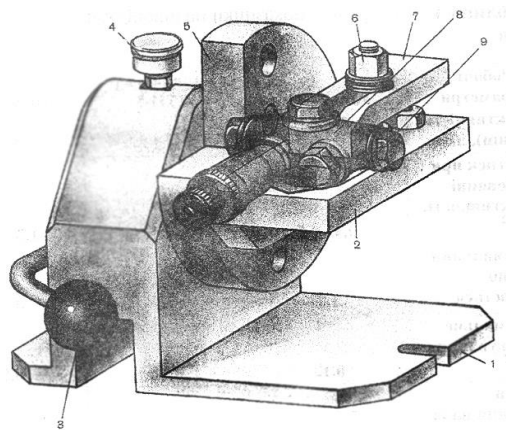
Пристрій для розбирання і складання паливо-підкачувальних насосів: 1 – корпус пристрою; 2 – опорна плита; 3 – рукоятка фіксатора; 4 – маслянка; 5 – поворотна планшайба; 6 – вузол кріплення; 7 – планка; 8 – паливопідкачувальний насос; 9 – підставка.
